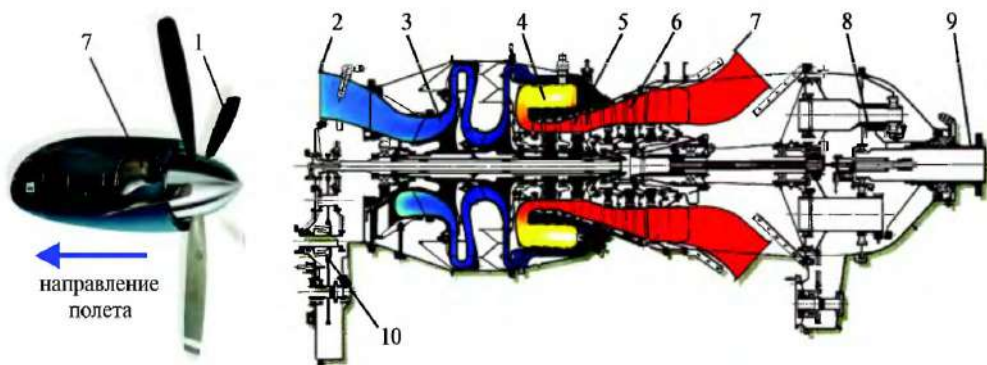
[3]. Общий вид и конструктивная схема ТВД с толкающим винтом (TRF-351-20): 1 – Толкающий винт; 2 – Входное устройство; 3 – Двухступенчатый центробежный компрессор; 4 –
